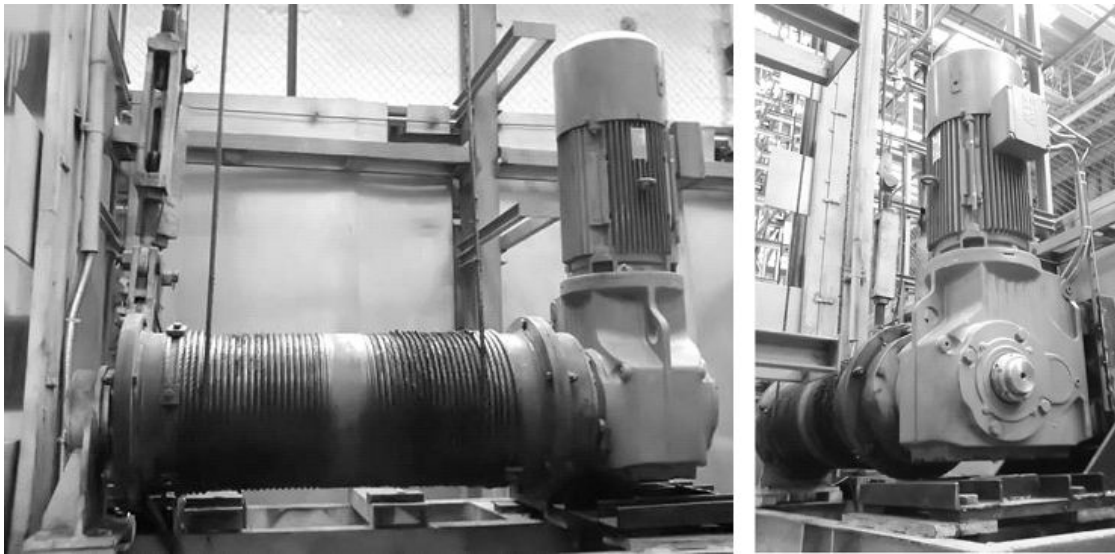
Барабан для підйому вантажозахватного пристрою
